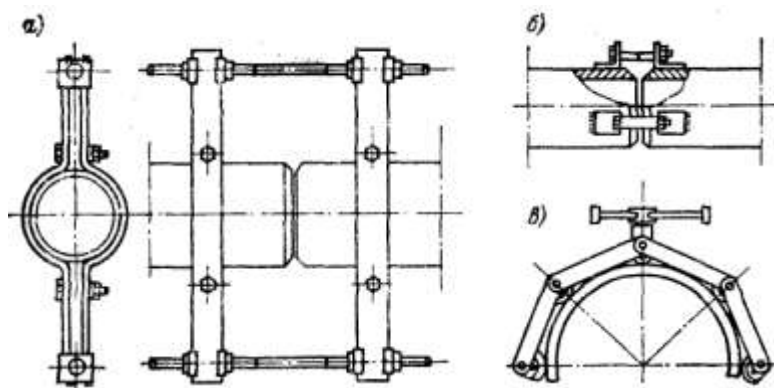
Приспособления для центровки труб а — хомутного типа; б — стяжные уголки; в — безмоментный наружный центратор
